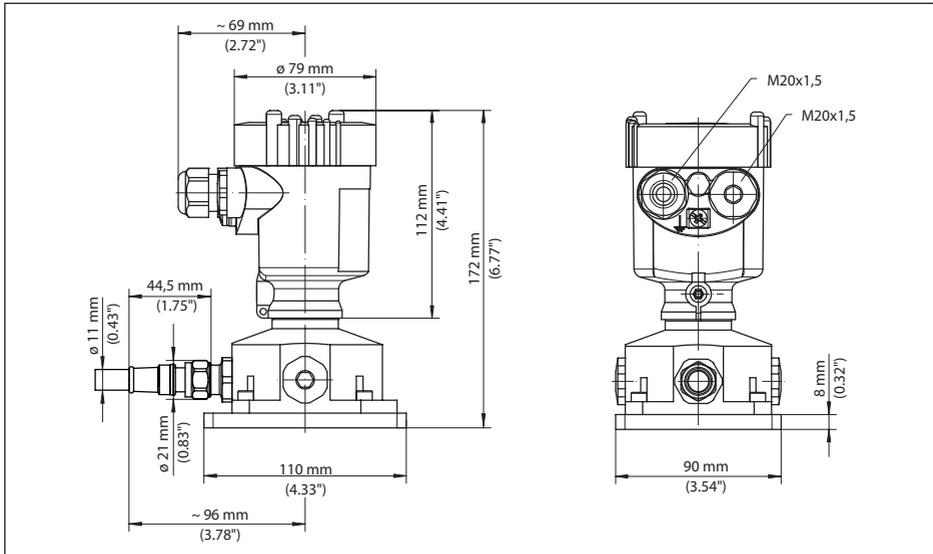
Gehäuseausführungen - Gerätegehäuse - Kunststoff oder Edelstahl (mit eingebautem PLICSCOM vergrößert sich die Gehäusehöhe um 9 mm/0.35 in)
